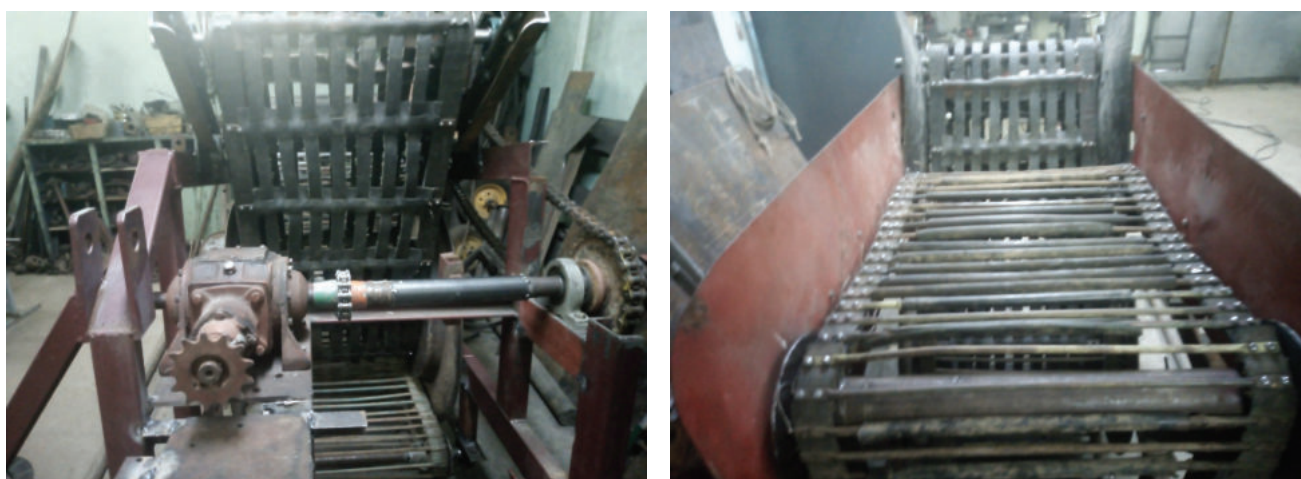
Элеваторы с поперечными ремнями, установленные на малогабаритный морковно-уборочный комбайн
